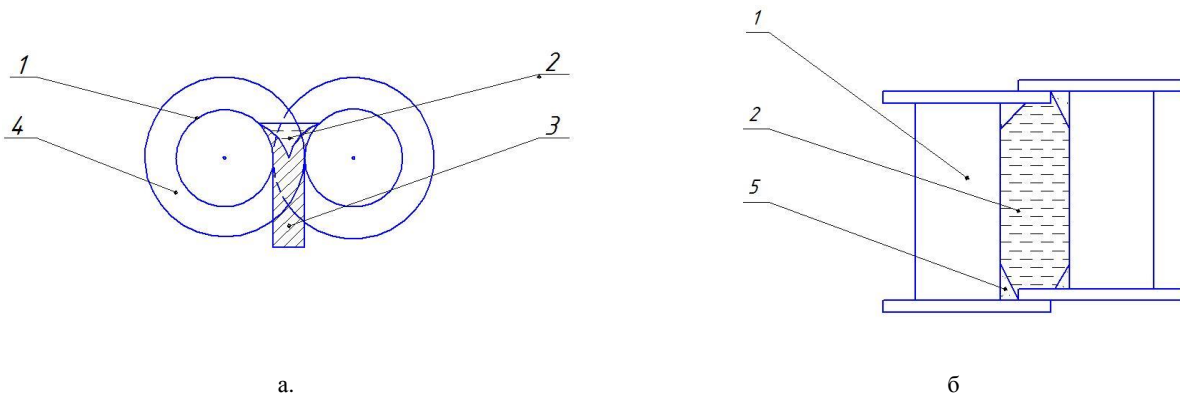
Ливарно-прокатна кліть [10]: а – вид з боку, б – вид зверху,
